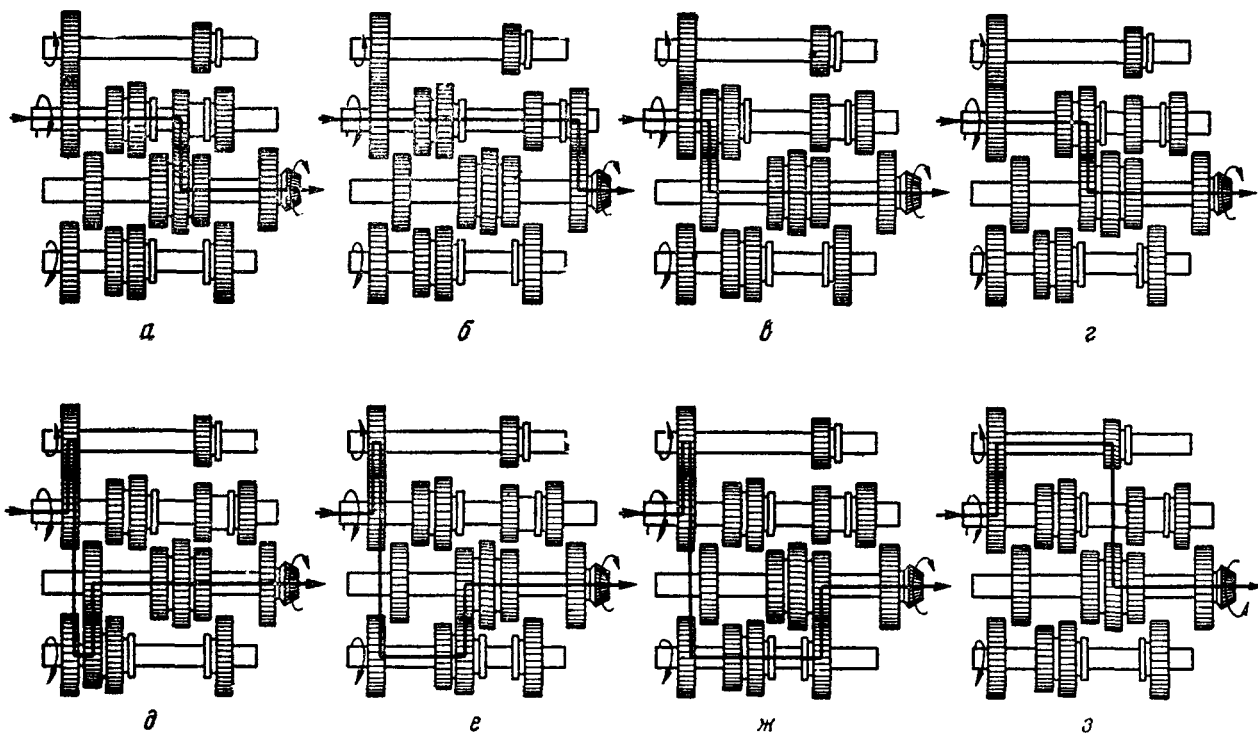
Схема расположения шестерен коробки передач при включенных передачах:
